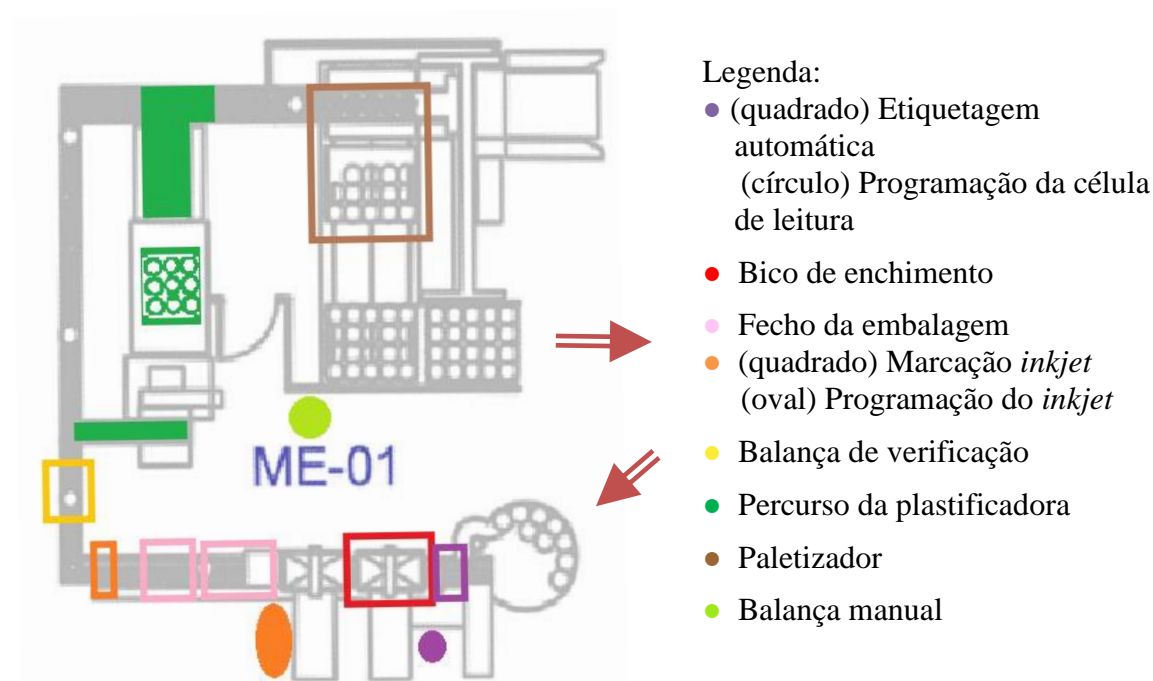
Planta da máquina ME01 e localização da zona de cada tarefa
